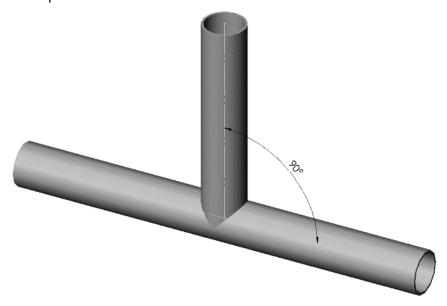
Jaula Antivuelco, Muestra de soldadura 1
